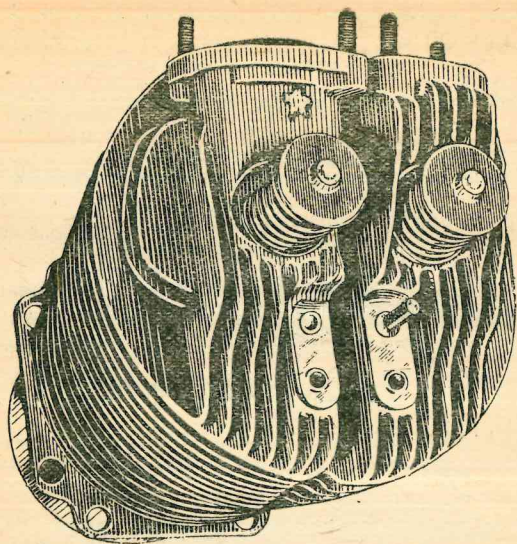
Цилиндр (шпильки крепления Т-образной стойки утеряны при движении)
